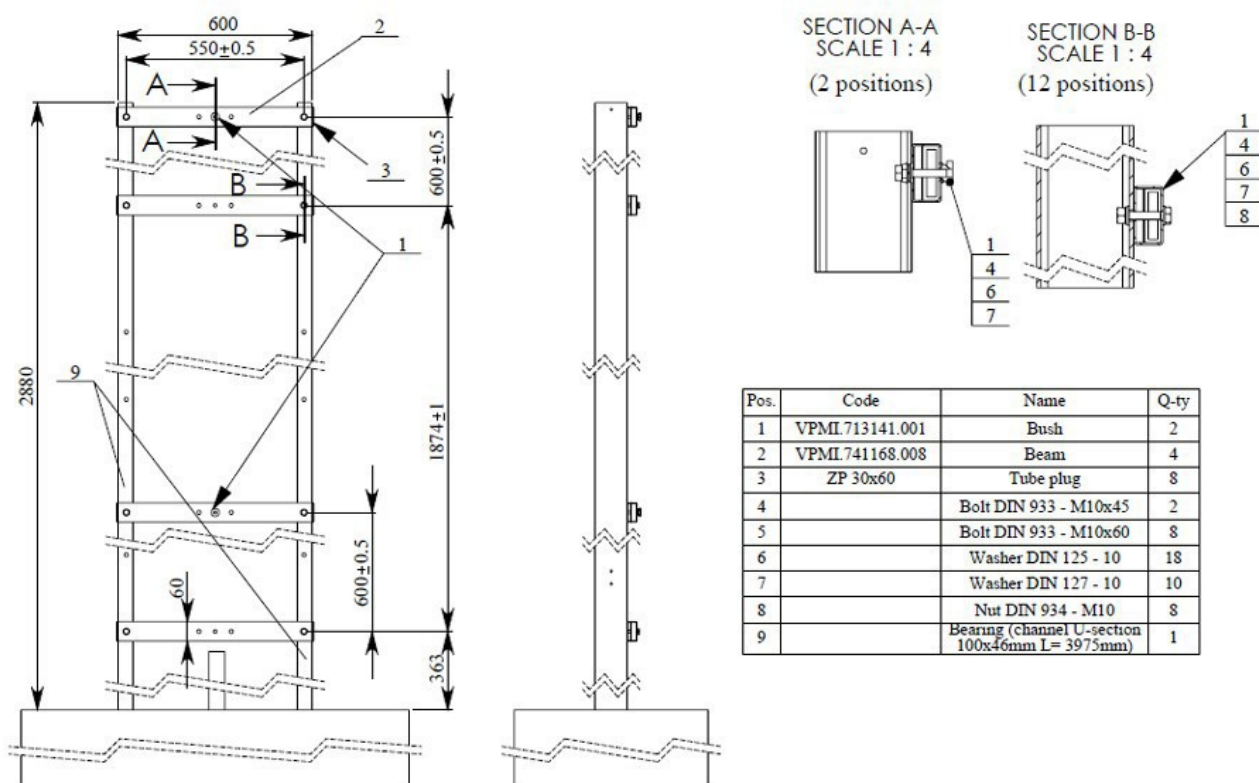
Montaje de vigas y casquillos en el pilar inferior de PoliGate Light G4
